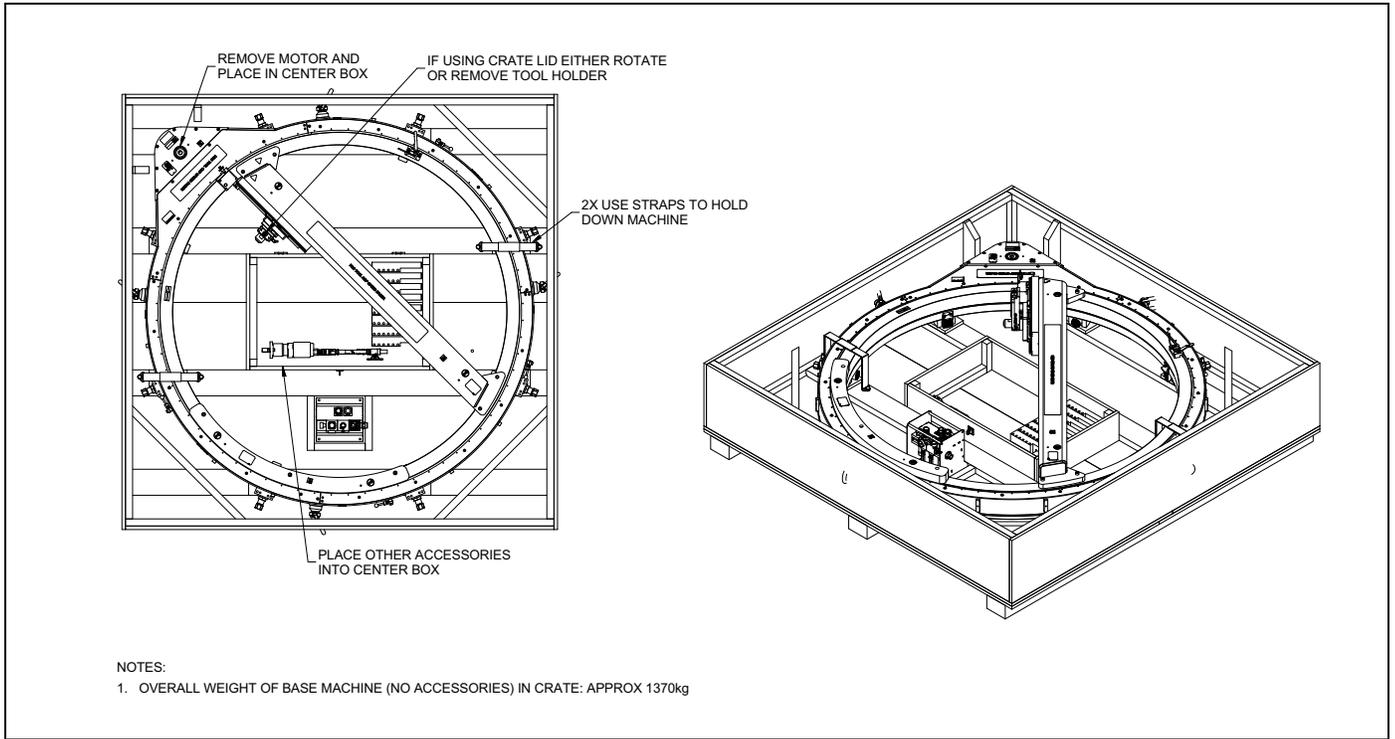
CAISSE D'EXPÉDITION DE LA MACHINE ODF60
